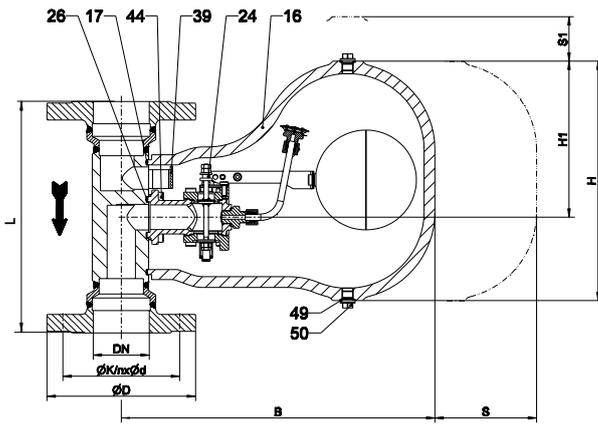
1 mit Flanschen - vertikale Einbaulage
